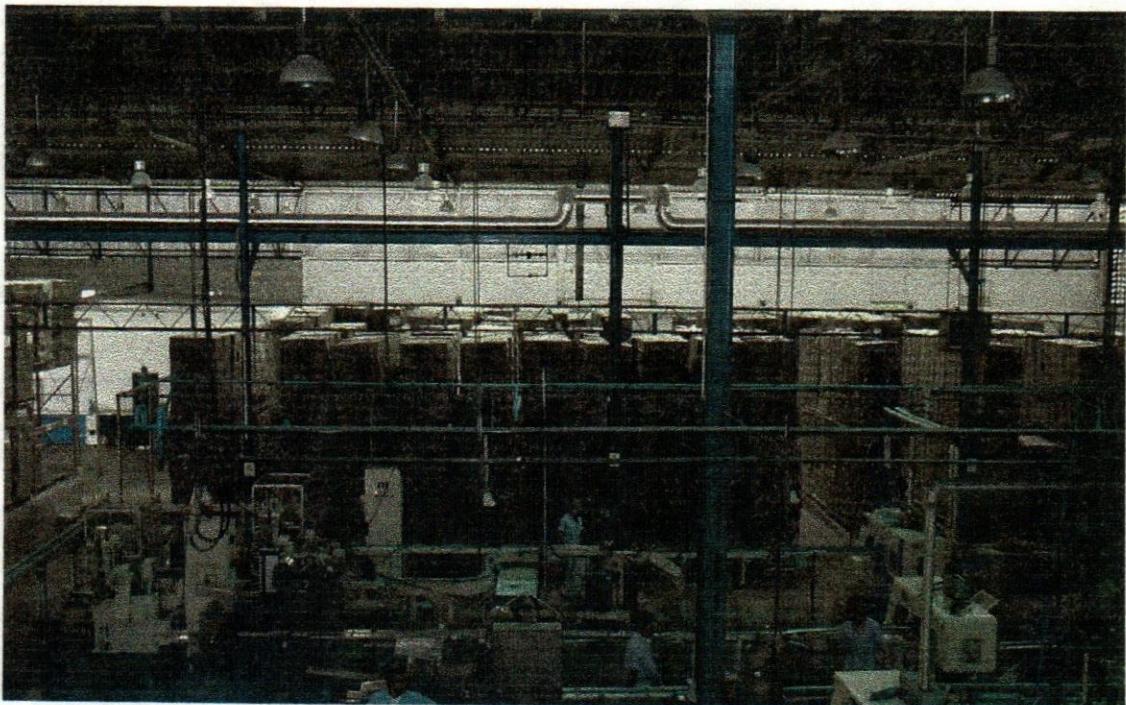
Vista del Area de Empaque (futura área para la instalación de las líneas)
